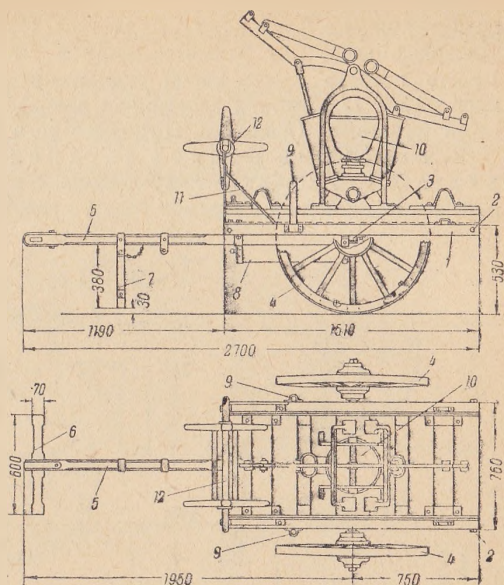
Насосный ручной двухколесный нерессорный ход.
